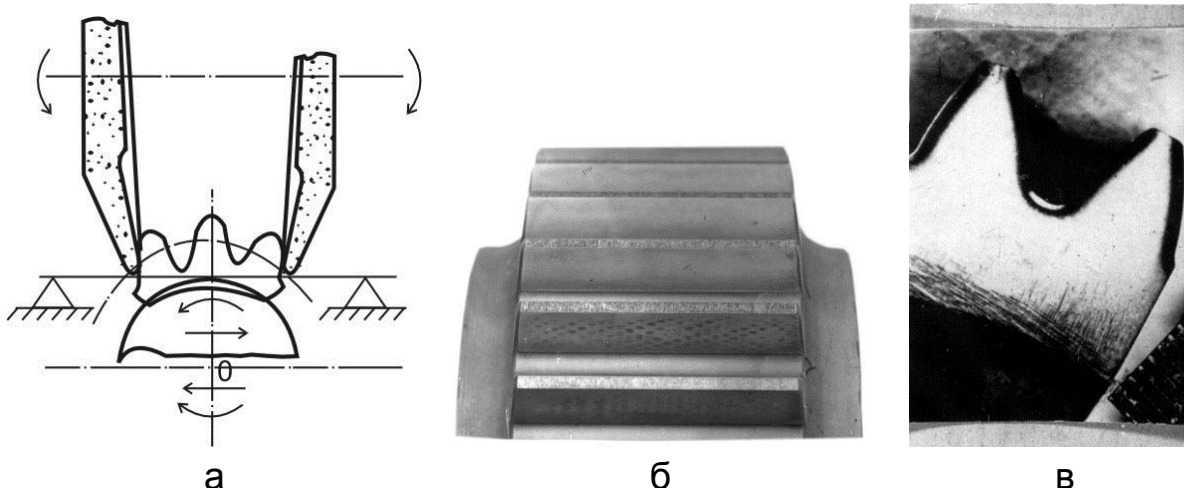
Схема шлифования зубчатого колеса на станке МААГ (5851): с нулевой настройкой кругов (а); внешний вид прижогов (б, в)
